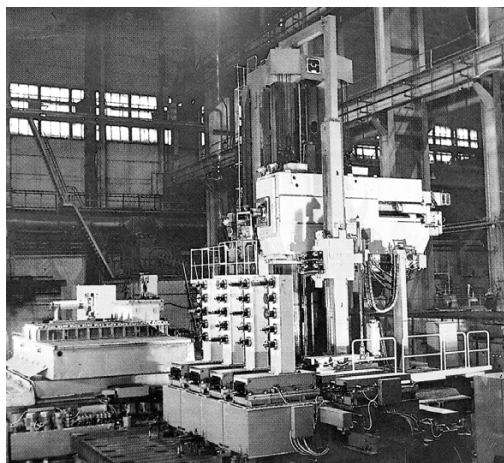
Тяжелый многоцелевой станок в составе: специальный фрезерно-расточный станок, поворотный стол, механизм смены оправок, система кассет и др.
